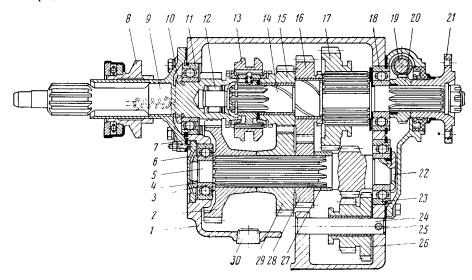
Коробка передач автомобиля УАЗ-451М:
